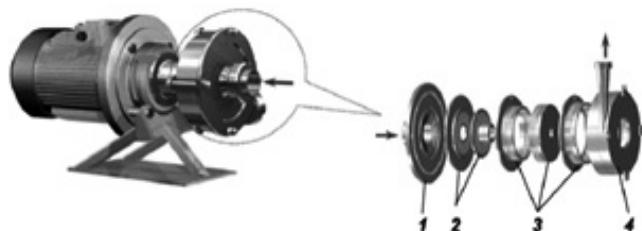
Корпусний роторно-пульсаційний апарат з дисковими елементами [37]: 1 — кришка; 2 — статорно-роторний дисковий вузол; 3 — статорно-роторний циліндричний вузол; 4 — корпус з вихідним патрубком
